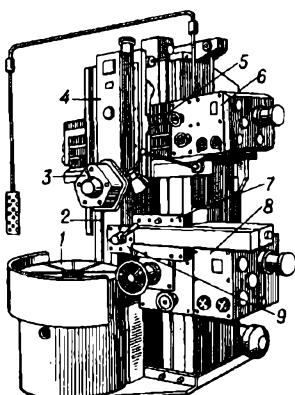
Токарно-карусельный станок: 1 – планшайба; 2 – станина с вертикальными направляющими; 3 – револьверная головка; 4 – вертикальный суппорт; 5 – поперечина; 6 и 8 – коробки подачи вертикального и бокового суппортов; 7 – боковой суппорт; 9 – резцедержатель
